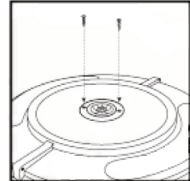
Drehen Sie die 2 Schrauben vorsichtig ein
